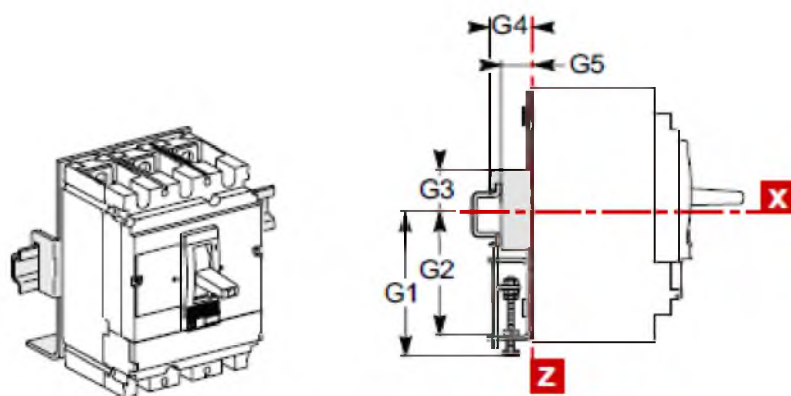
Установочные размеры ВА-СЭЦ-МС100/160/250 на DIN - рейке
